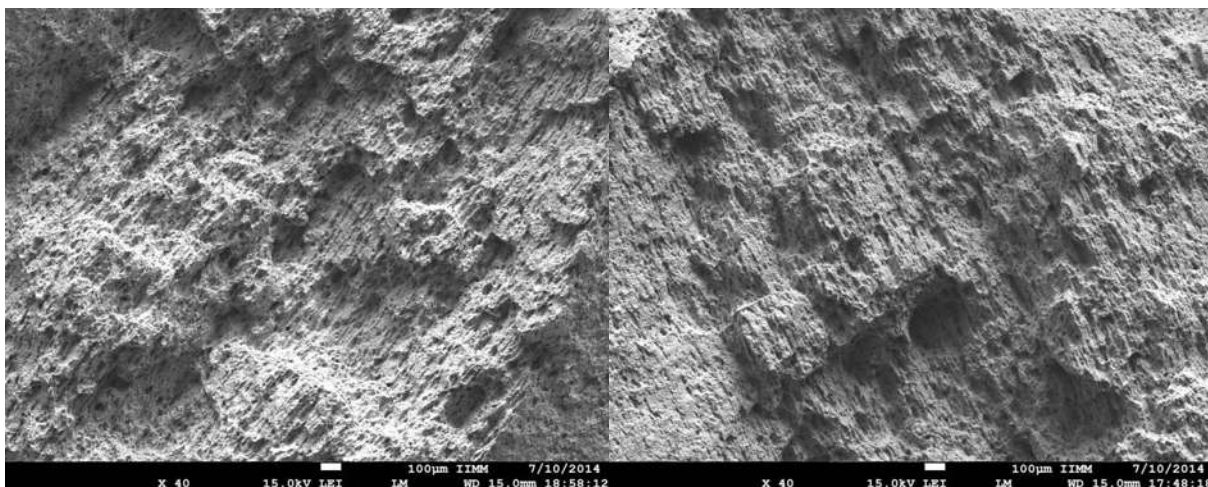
22.- Fractografía de la soldadura 4-1(cordón de auto-revenido, condición 1).
